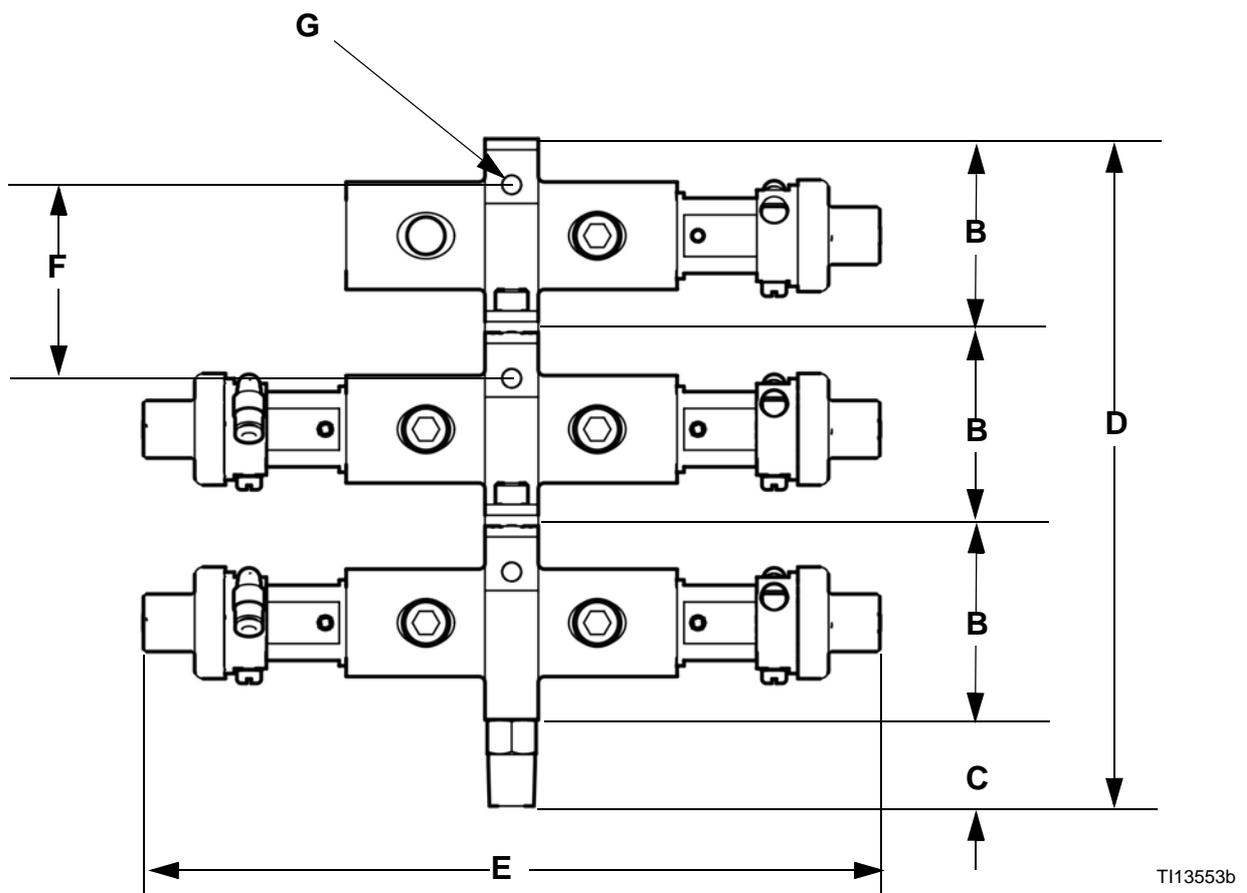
Dimensiones de pila de válvulas de baja presión - Serie B
